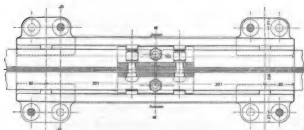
Grundriß der Brücke (1/2 nat. Größe).
